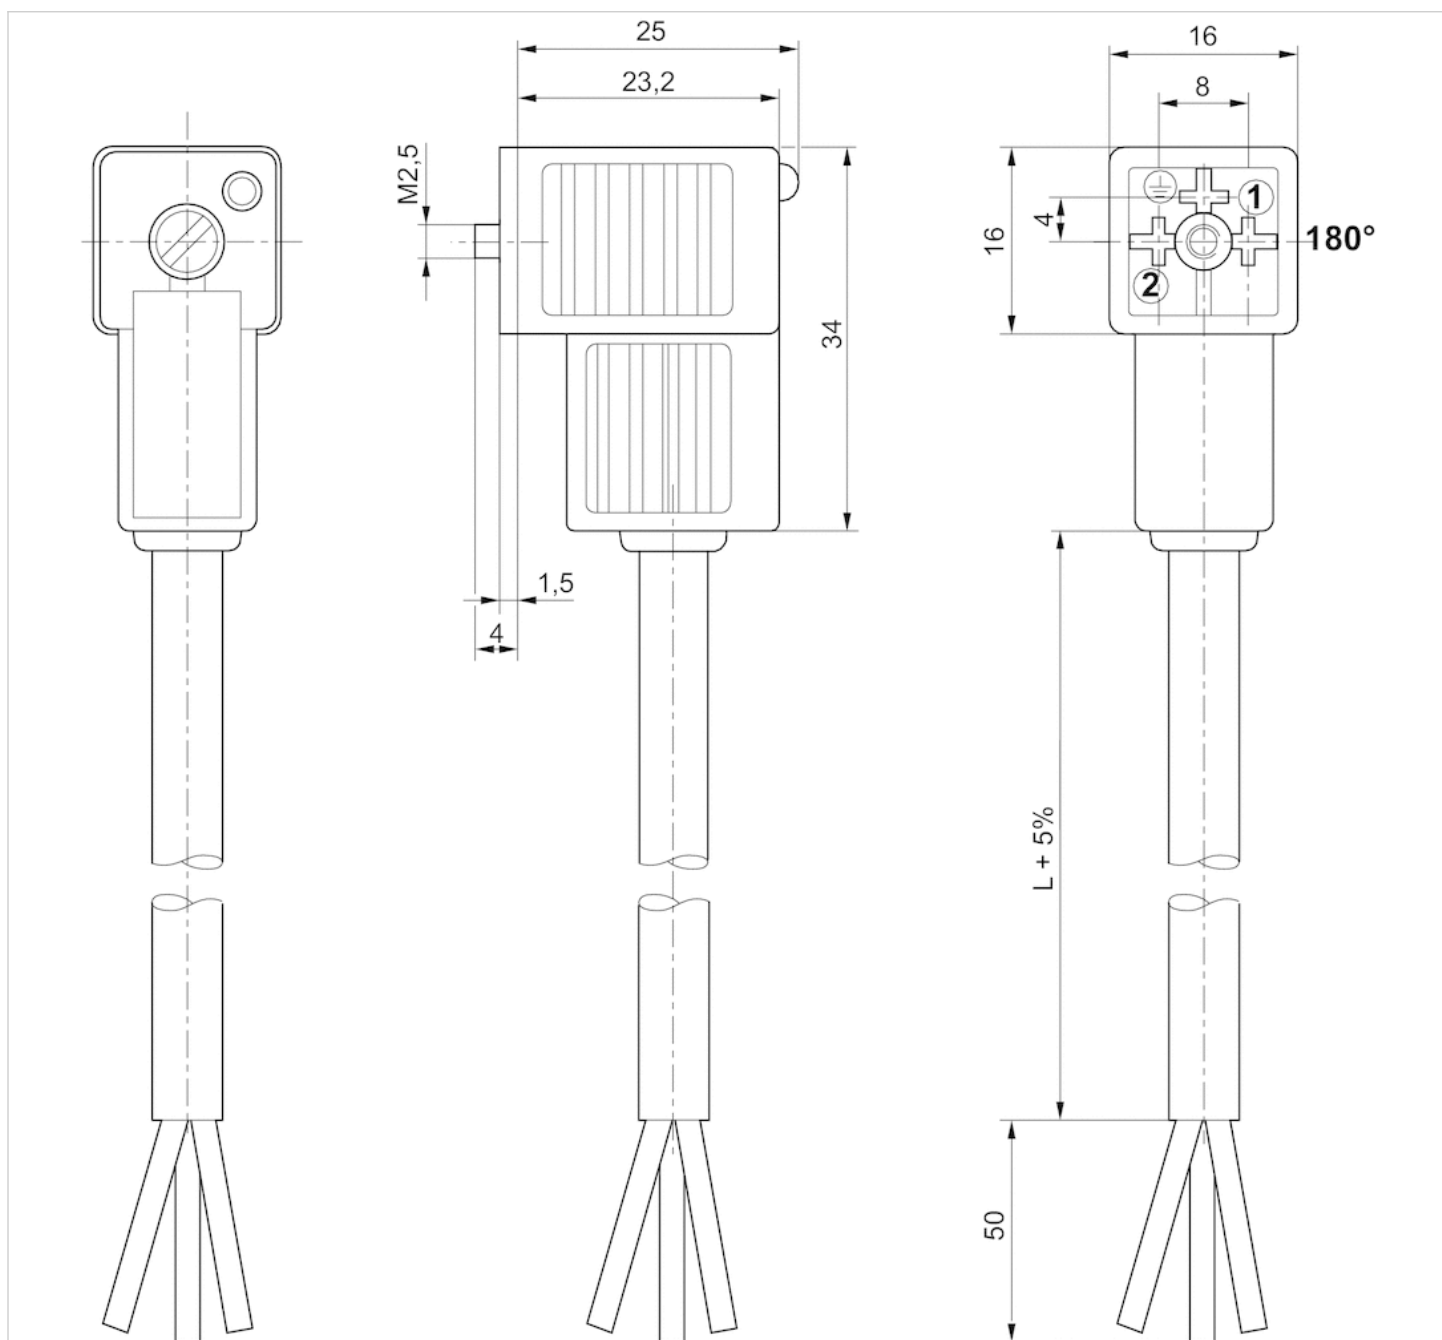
, Dimensions en mm, Cartouche de douille à 180° ?
